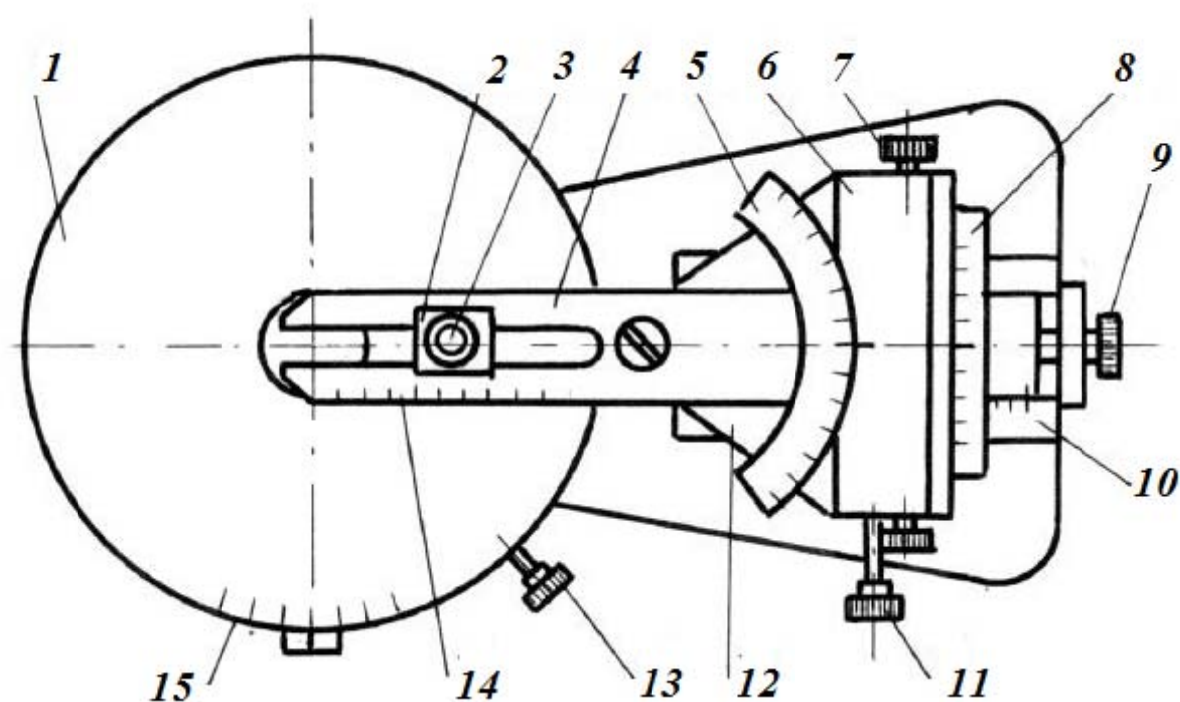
Схема прибора для вычерчивания теоретического профиля кулачка
